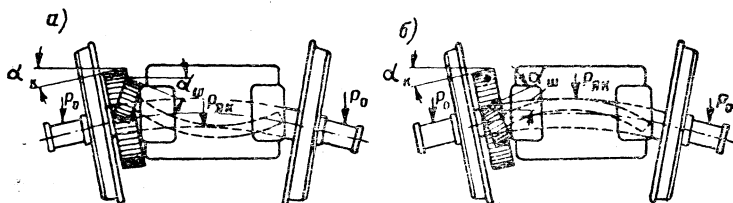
Схема взаимного положения шестерни и зубчатого колеса тепловозов при движении:
